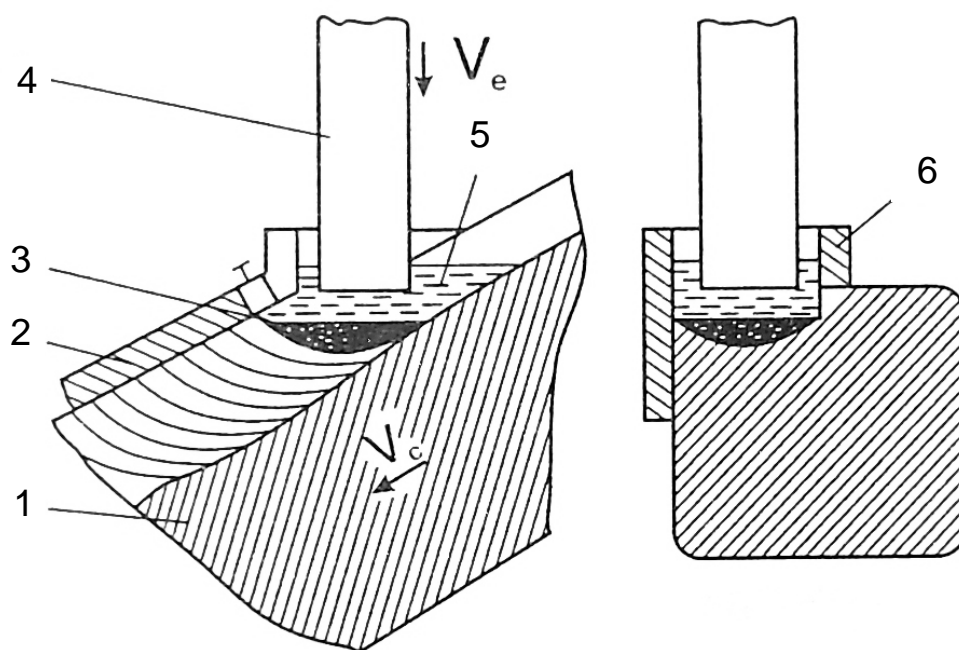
ЭШН заготовок под прокатку сортового биметалла с наклонным расположением наплавляемой поверхности:
